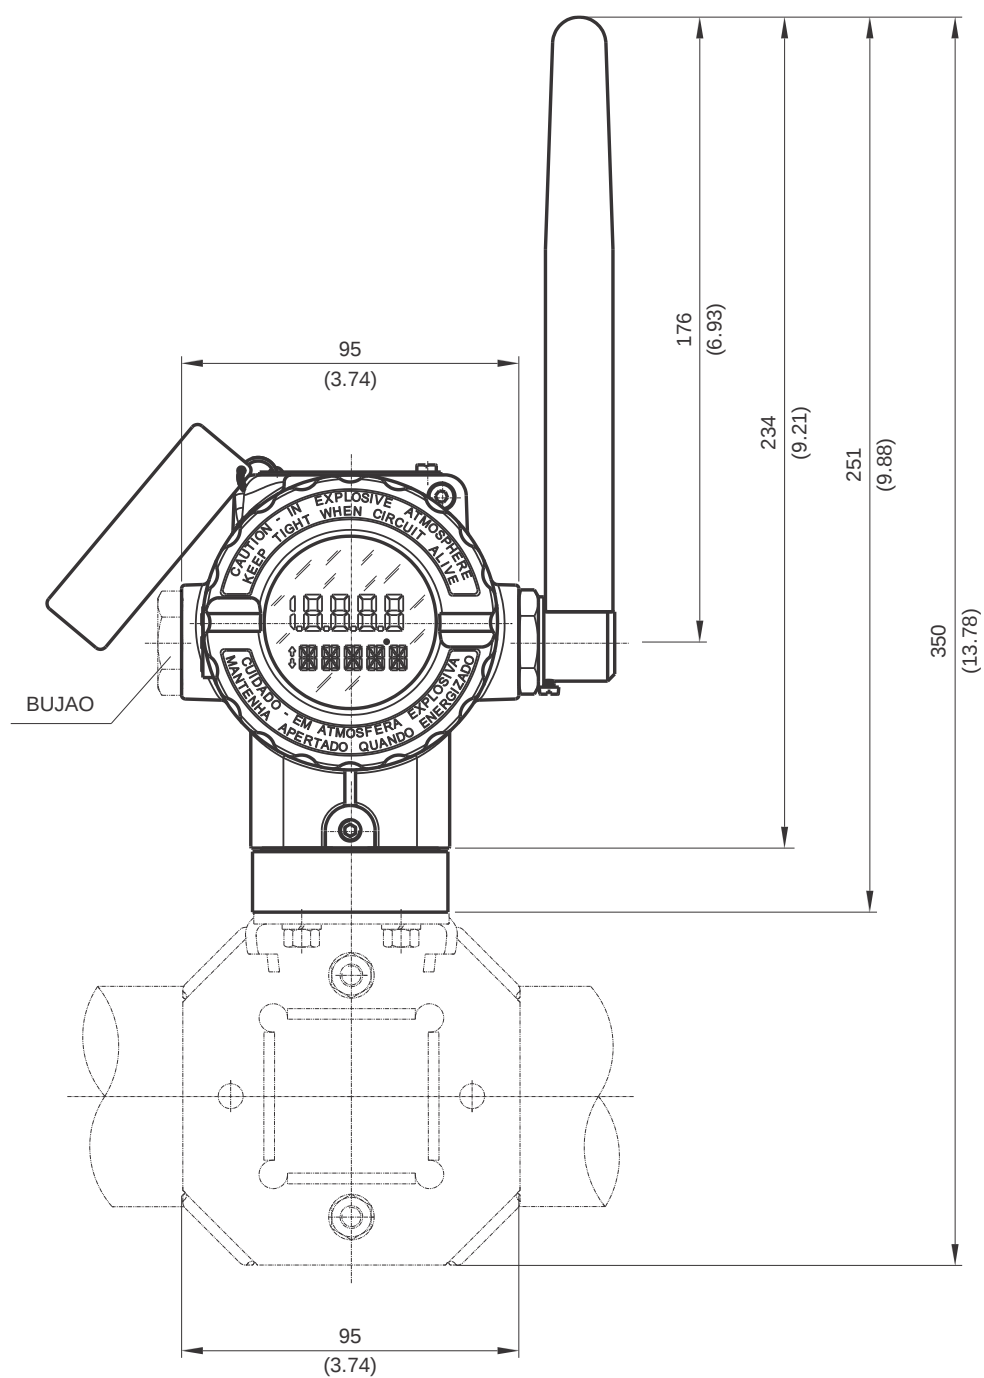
2 – Desenho Dimensional de Montagem do RP400 WirelessHART® na vertical
